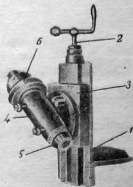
Патрон Квиаль с делительным приспособлением.
